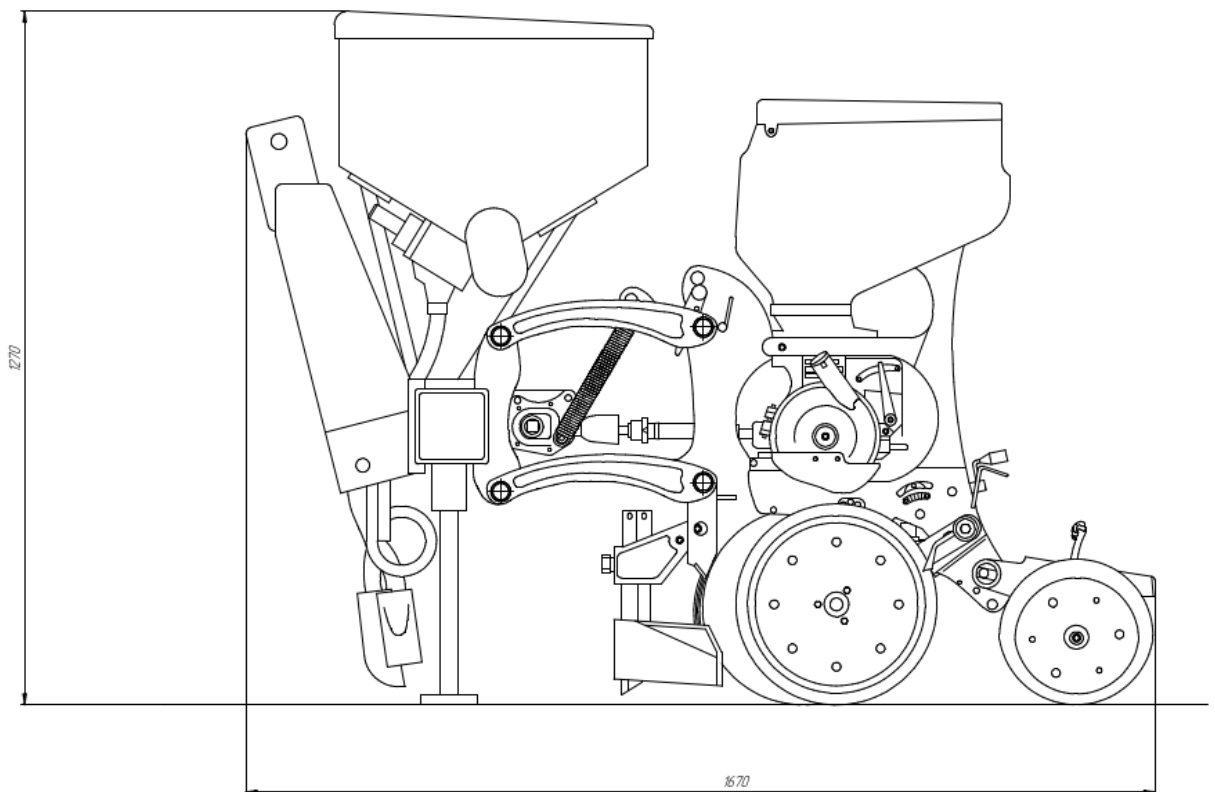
Загальний вид сівалки Gaspardo MTR-8
